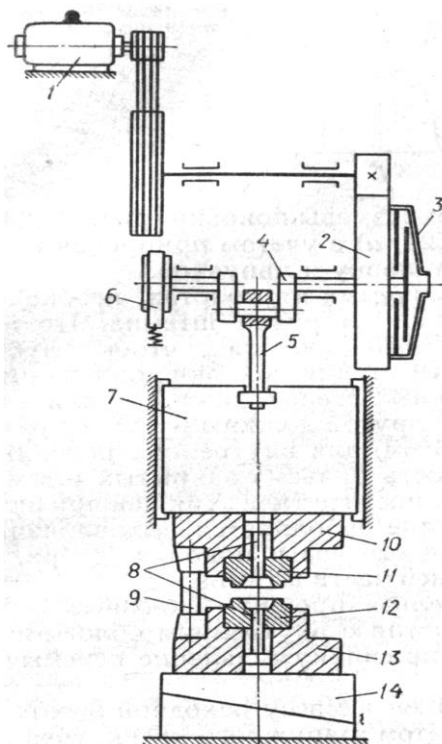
Схема кривошипного горячештамповочного прессы
